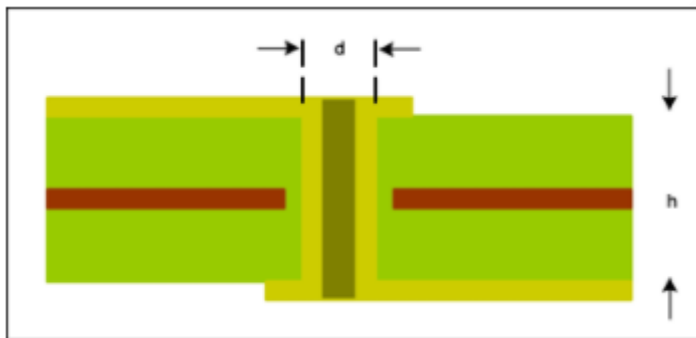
PCB 横截面用于估算寄生影响的过孔结构。
